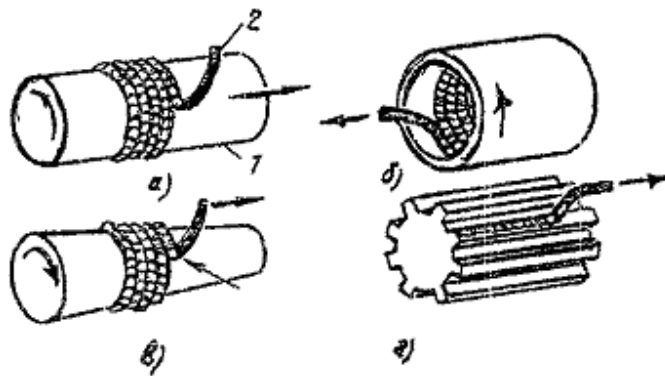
Схема вібродугового наплавлення зношених поверхонь
